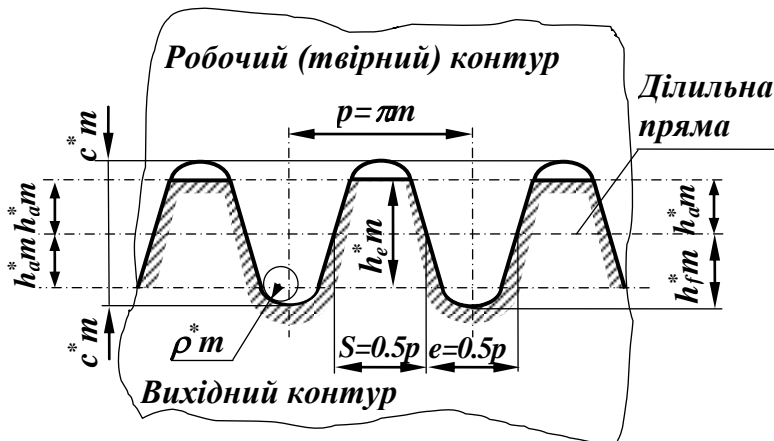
Вихідний і робочий контури інструментальної рейки
